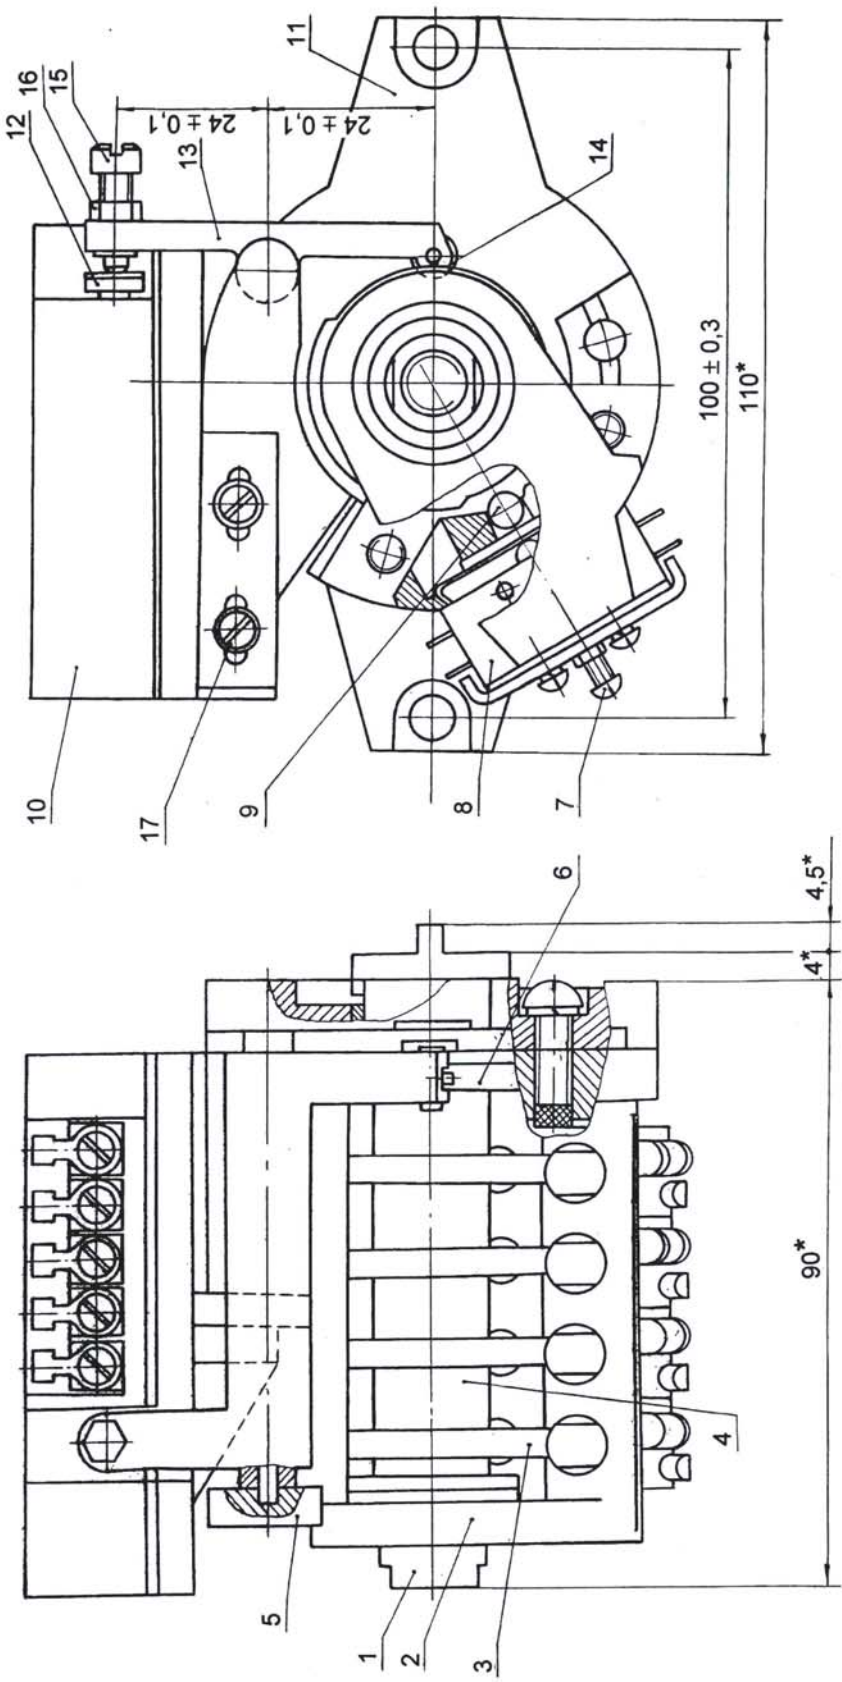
Общий вид и габаритные и присоединительные размеры блока датчика БСПТ -10М
